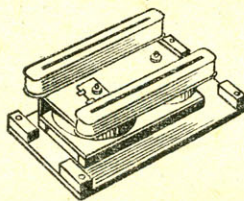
Датчик-звукосниматель: а — конструкция; 1 — пластинки-магнитопроводы; 2 — ферритовые кольцевые магниты; 3 — катушки; 4 — бруски из оргстекла; 5 — болты М3; 6 — основание; 7 — бруски пористой резины; 8 — пластинка с монтажными лепестками.
